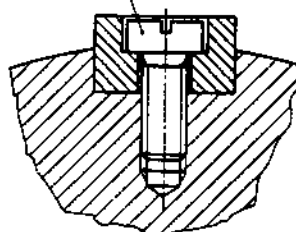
Fissaggio di linguetta nella cava dell'albero, ottenuta impiegando vite a testa cilindrica con intaglio.
